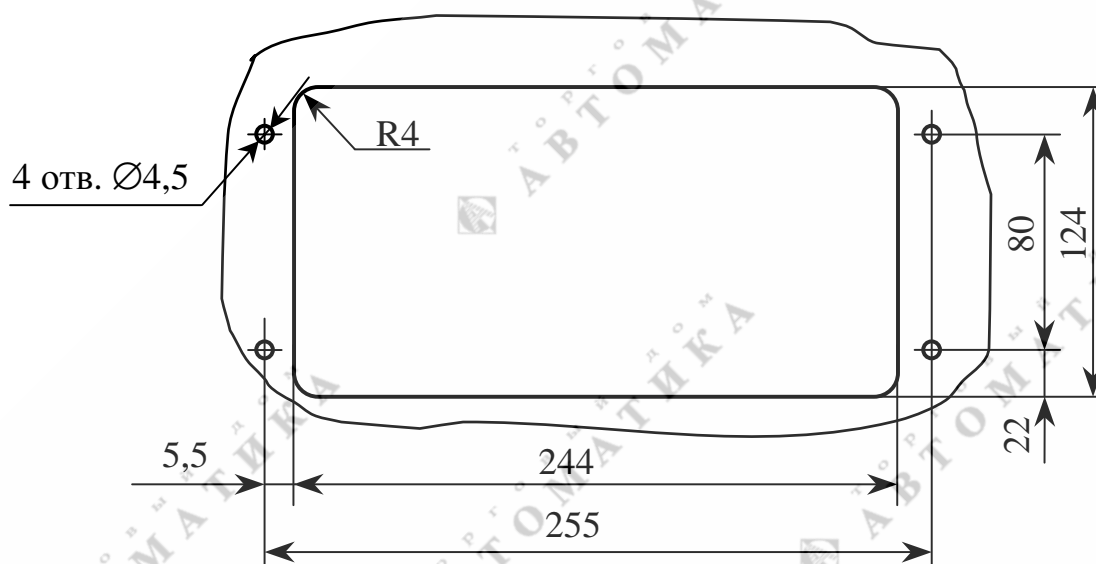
Разметка отверстий для крепления блока преобразовательного щитового исполнения
